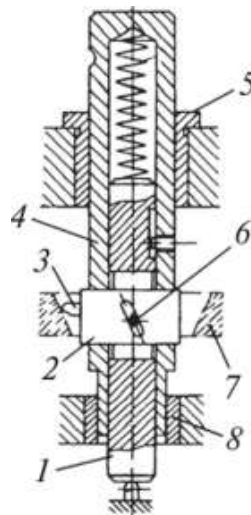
Схема пристрою для переміщення різального інструменту (розточування конічного отвору)
